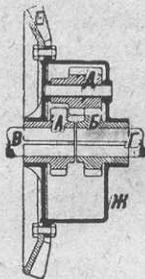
Дифференциал с цилиндрическими зубчатками.
